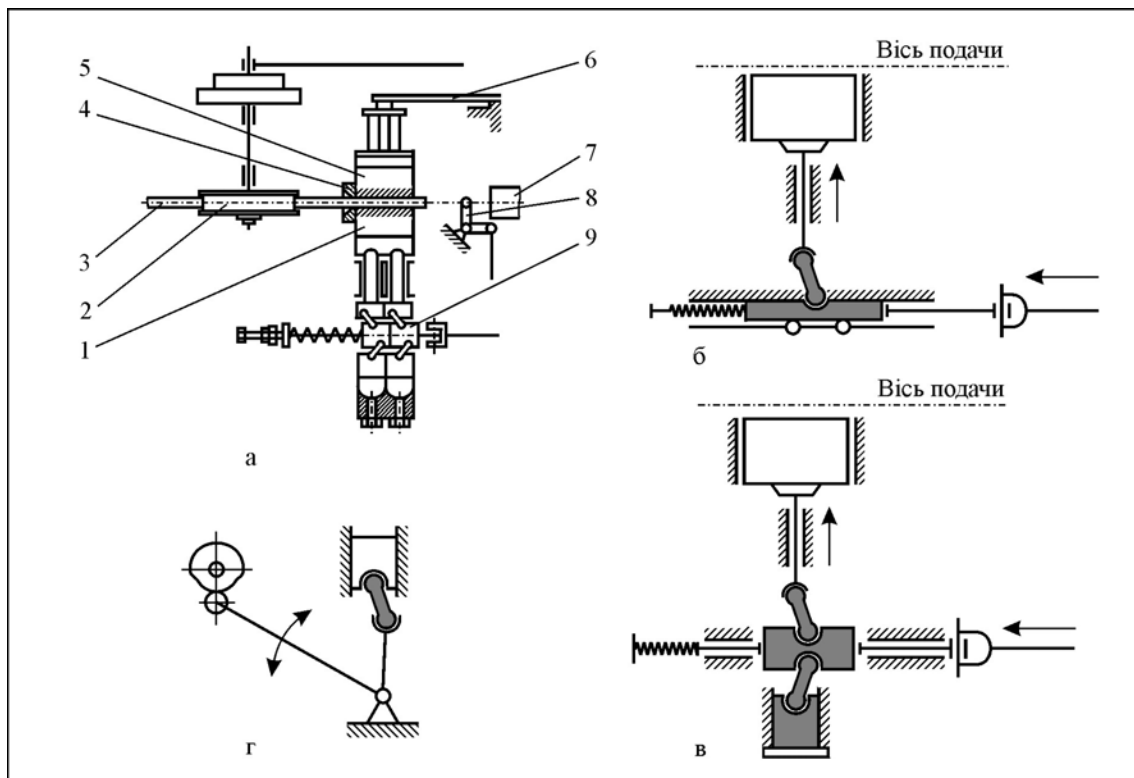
Кінематична схема затиснення та відрізування заготовки холодновисаджувального автомата з рознімною матрицею (а): 1 – нижня напівматриця; 2 – ролики; 3 – дріт; 4 – відрізна матриця; 5 – верхня напівматриця; 6 – пружина; 7 – пуансон; 8 – поворотний упор; 9 – колінний важіль. Колінноважільні системи механізмів відрізування та затиснення заготовок : б – однобічного типу; в – двобічного типу; в – гойдального типу
